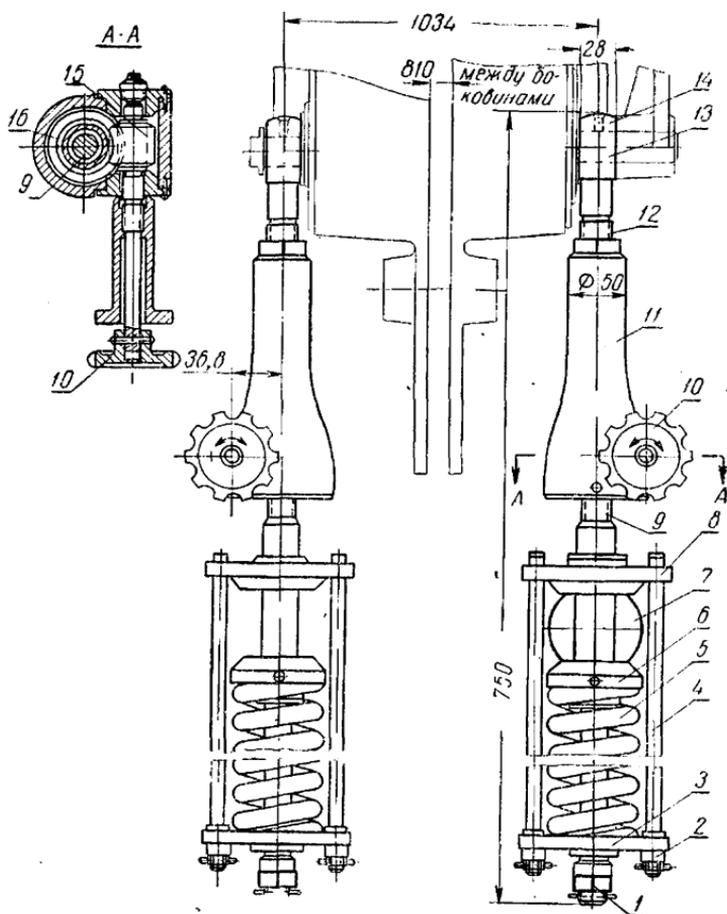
Механизм настройки параллельности валцов станка 3С.
